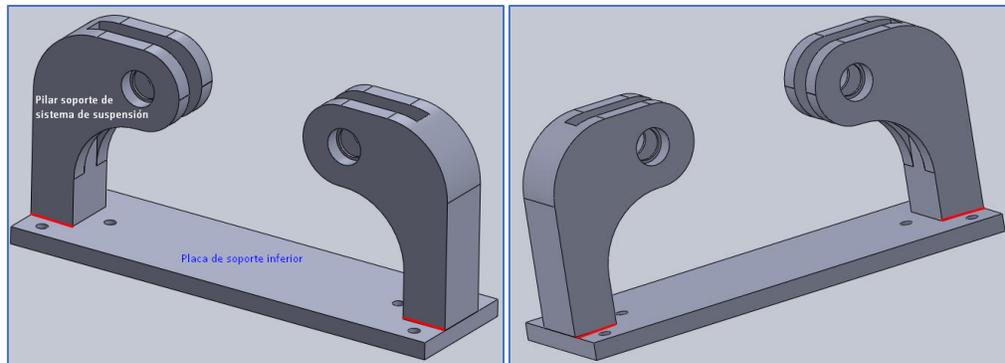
Ubicación del cordón de soldadura entre la placa soporte inferior y las columnas de sujeción. Fuente: Elaboración propia.
